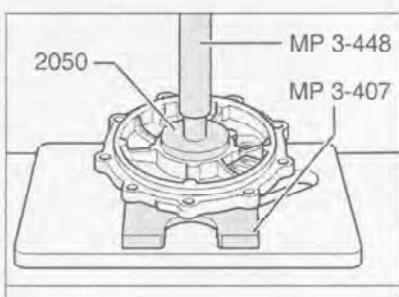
Установка наружной обоймы роликоподшипника в крышке.
